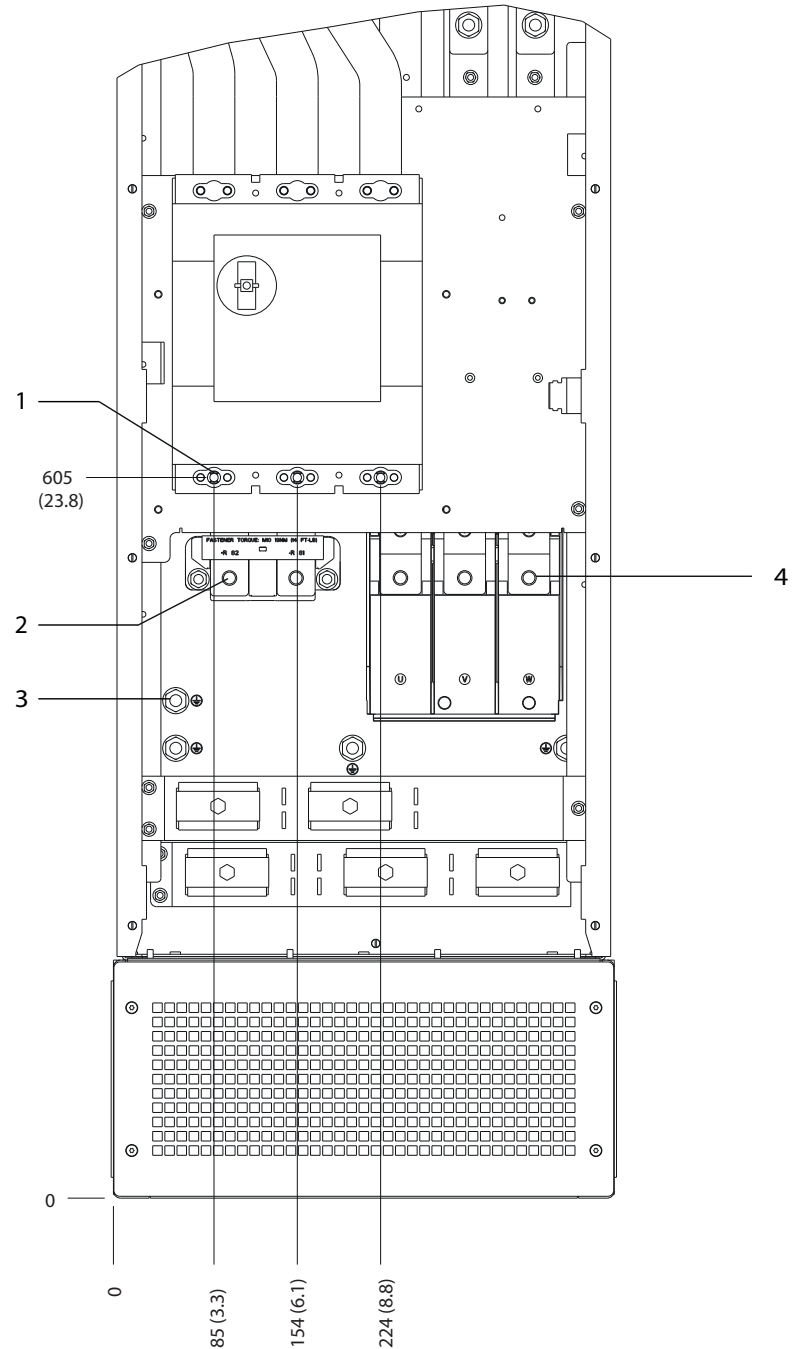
Dimensions des bornes D8h avec options contacteur et sectionneur (vue frontale)
